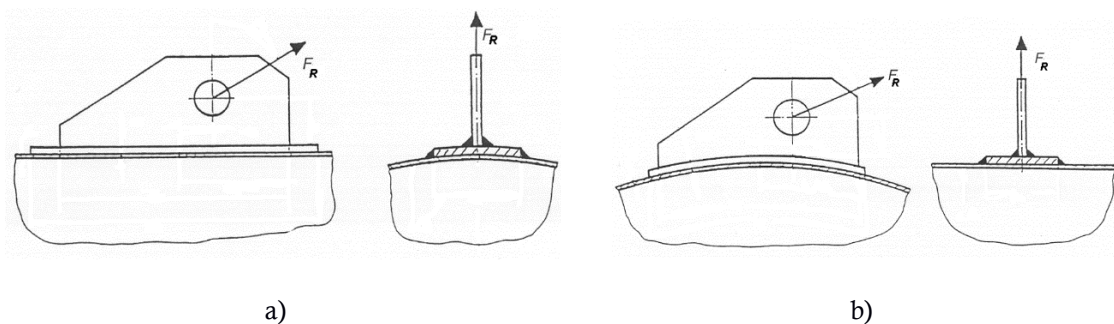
Pontos de elevação com disposição longitudinal (a) [19] e tangencial (b) [19]
